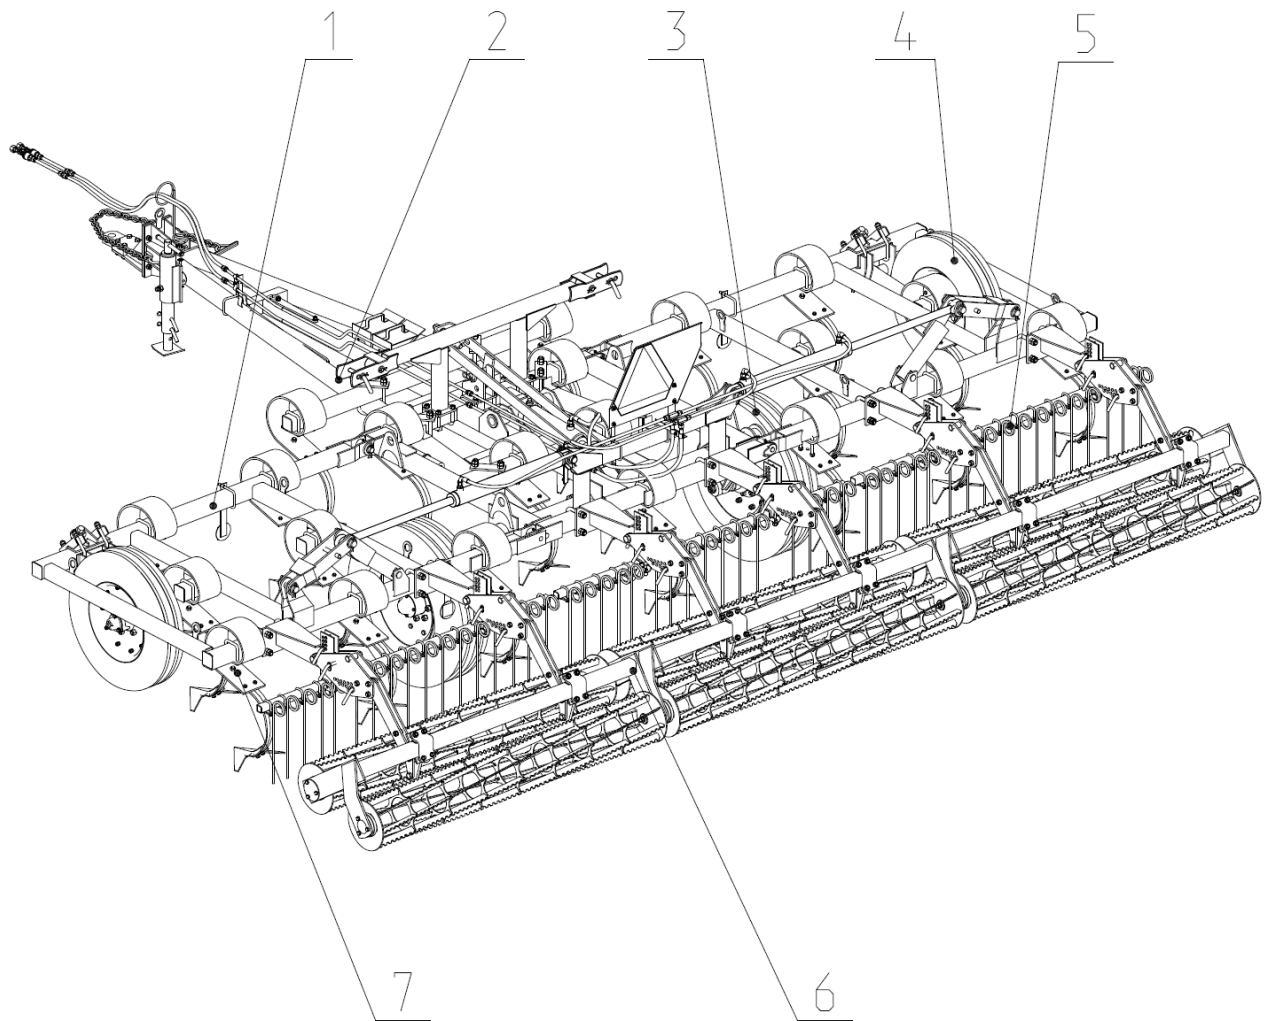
КСП-6 К1 Культиватор с комплектом 2-х рядных катков и однорядной гребенки. 1-КСП 01.090Б, КПС 01.090Б-01 Крыло; 2-КСП 02.000Б Сница; 3-КСП 03.000А Колесная пара; 4- КПС 03.030 и КПС 03.030-01 Колесо опорное; 5-Однорядная гребенка; 6- 2-х рядные катки прикатывающиеся; 7- КШУ 17.000 Подвеска.
